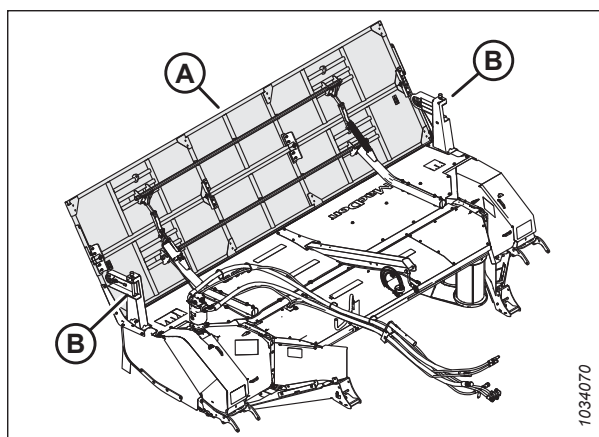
Противоосыпательный щиток и фонари — рабочее положение
